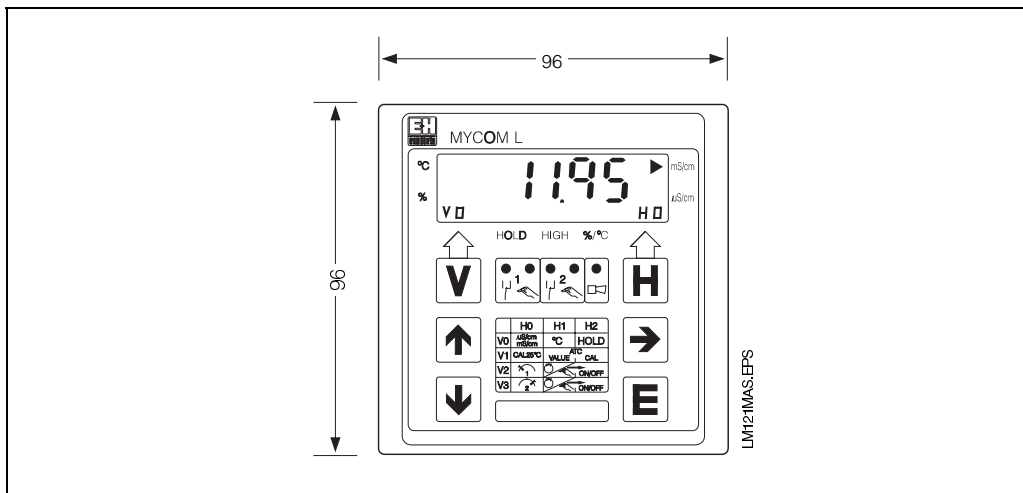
Dimensions du transmetteur Mycom CLM 121
